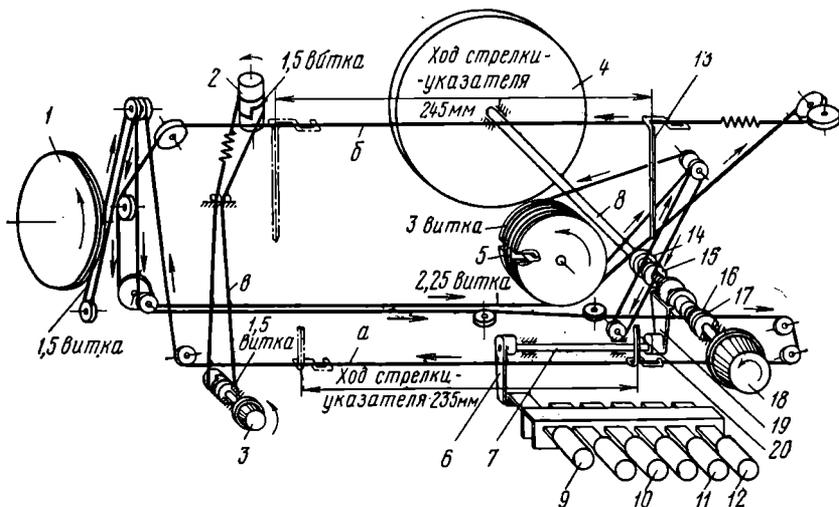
Кинематическая схема верньерного устройства блока настройки:
